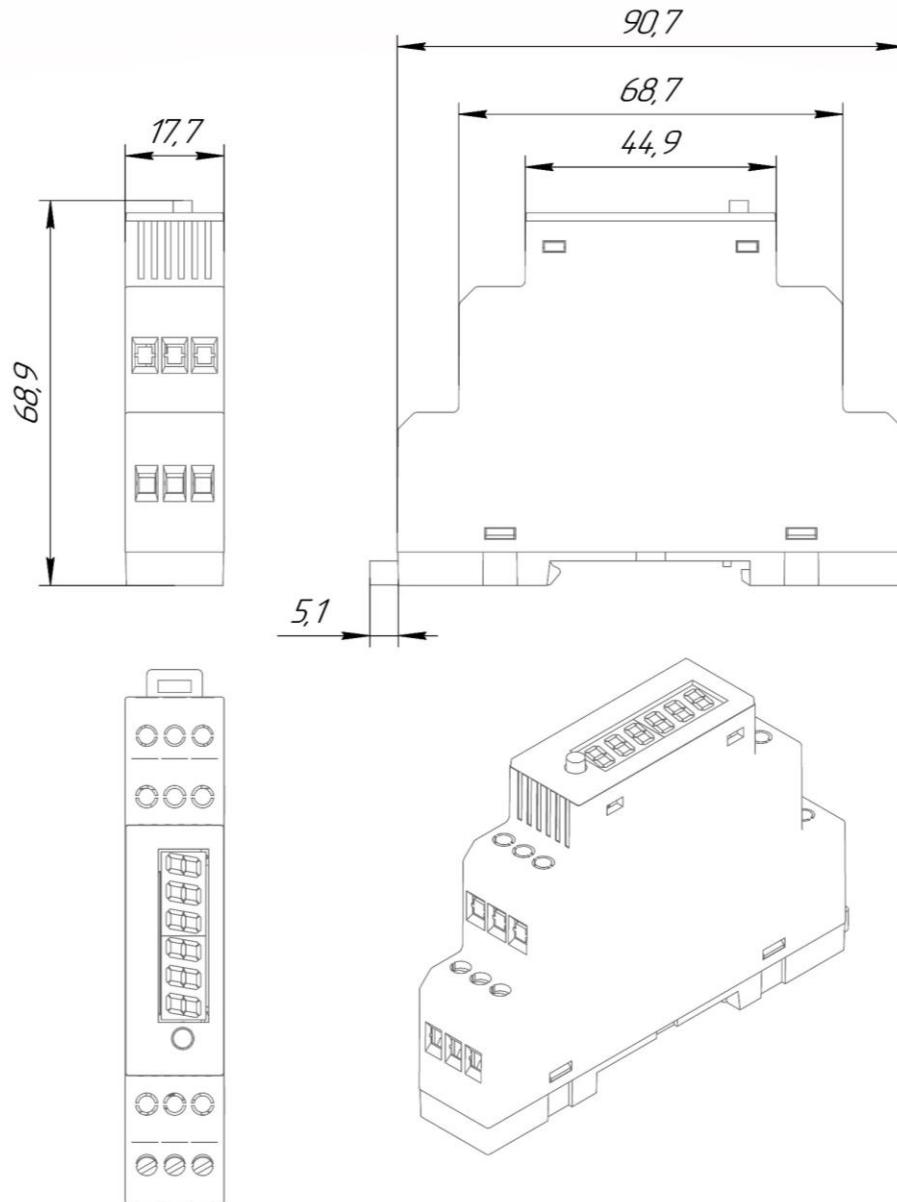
Габаритные размеры счётчика моточасов WTM-02
